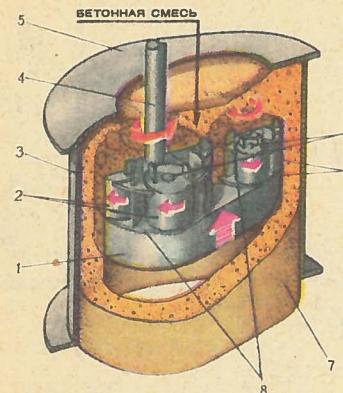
Формование овощадальных труб парой катковых устройств разного диаметра. Цифрами обозначены: 1 — поддон, 2 — вальцы, 3 — обечайка, 4 — вал, 5 — съемная пластина, 6 — оси катков, 7 — готовое изделие, 8 — вальцевые головки.
